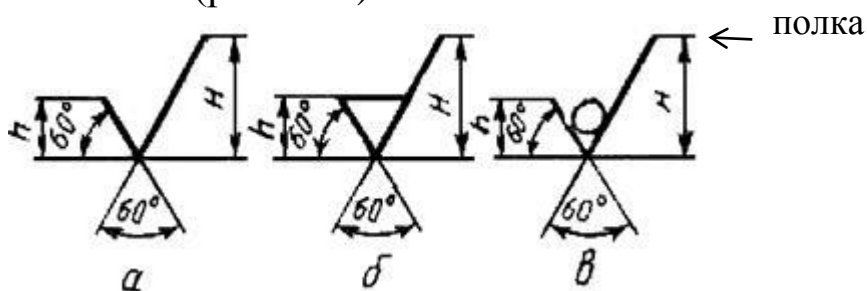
Обозначение шероховатости поверхности: а – способ обеспечения шероховатости конструктором не устанавливается; б – шероховатость обеспечивается удалением слоя материала; в – шероховатость образована без удаления слоя материала;  $h$  – 5 мм.;  $H$  – 10 мм. Длина полки соответствует длине записи. Например,  $R_a 2,5$  мкм.
